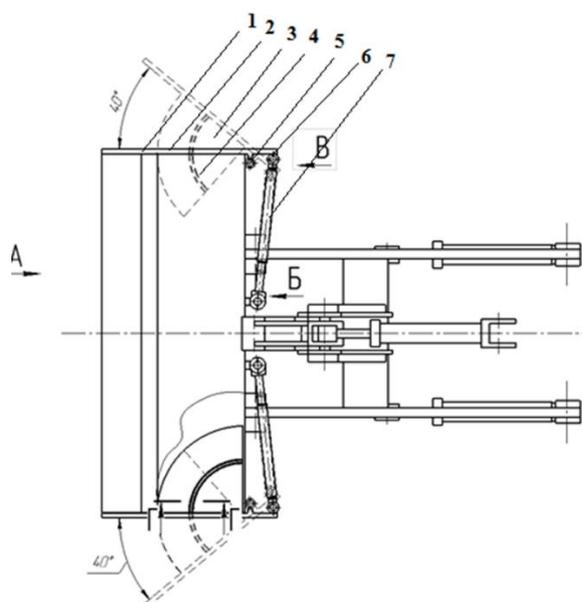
Конструкция ковша рабочего органа погрузчика на примере «Амкодор 333»: 1 – ковш, 2 – поворотная боковина ковша, 3 – сегмент, 4 – направляющая, 5 – ухо ковша и боковины, 6 – ухо боковины и гидроцилиндра, 7 – гидроцилиндр
